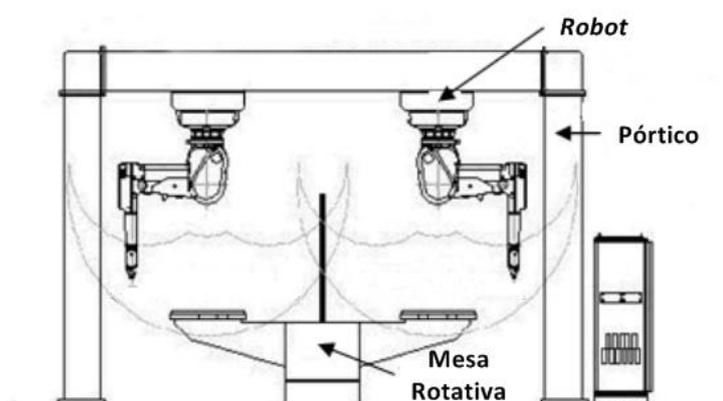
Esquema de pórtico de soldadura. Adaptado de:(4)
